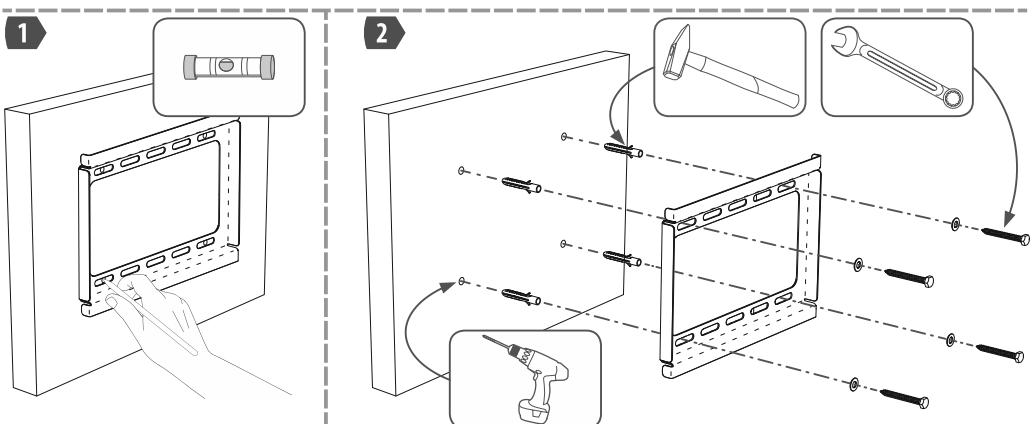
Установка несущей панели на стену (показан вариант монтажа на бетонную или кирпичную стены).
